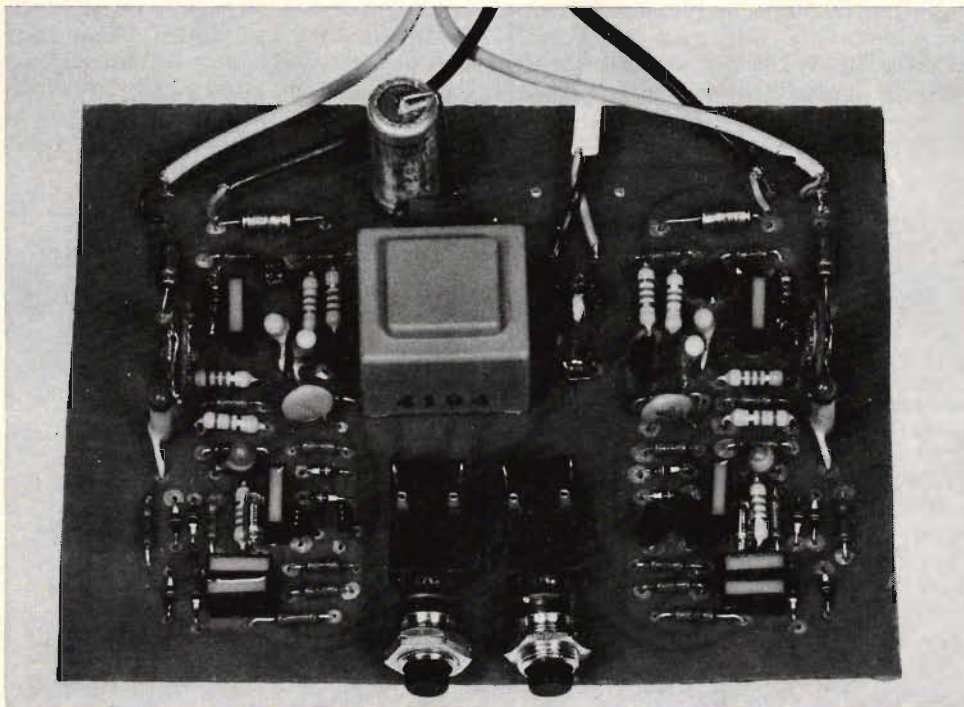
Bilden visar en tidig prototyp till RTs DNL-enhet. Jämfört med fig 9 fattas några komponenter i nätdelen. Kortets dimensioner har också senare gjorts mindre.
